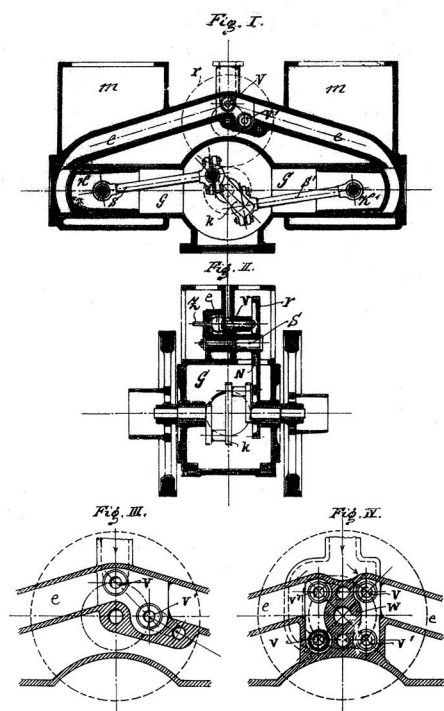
Фрагмент из французского патента Б. Г. Луцкого № 248989 «Газовая и углеводородная машина с двумя цилиндрами, размещенными друг напротив друга, и кривошипами, расположенными под углом 180° »
